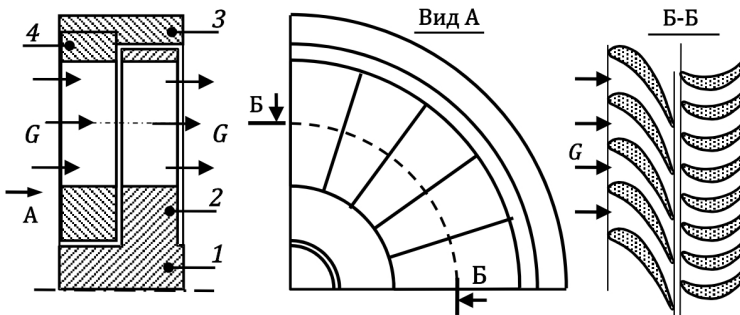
Турбинная ступень: 1 – ротор; 2 – рабочая лопатка; 3 – корпус турбины; 4 – сопловая решетка
